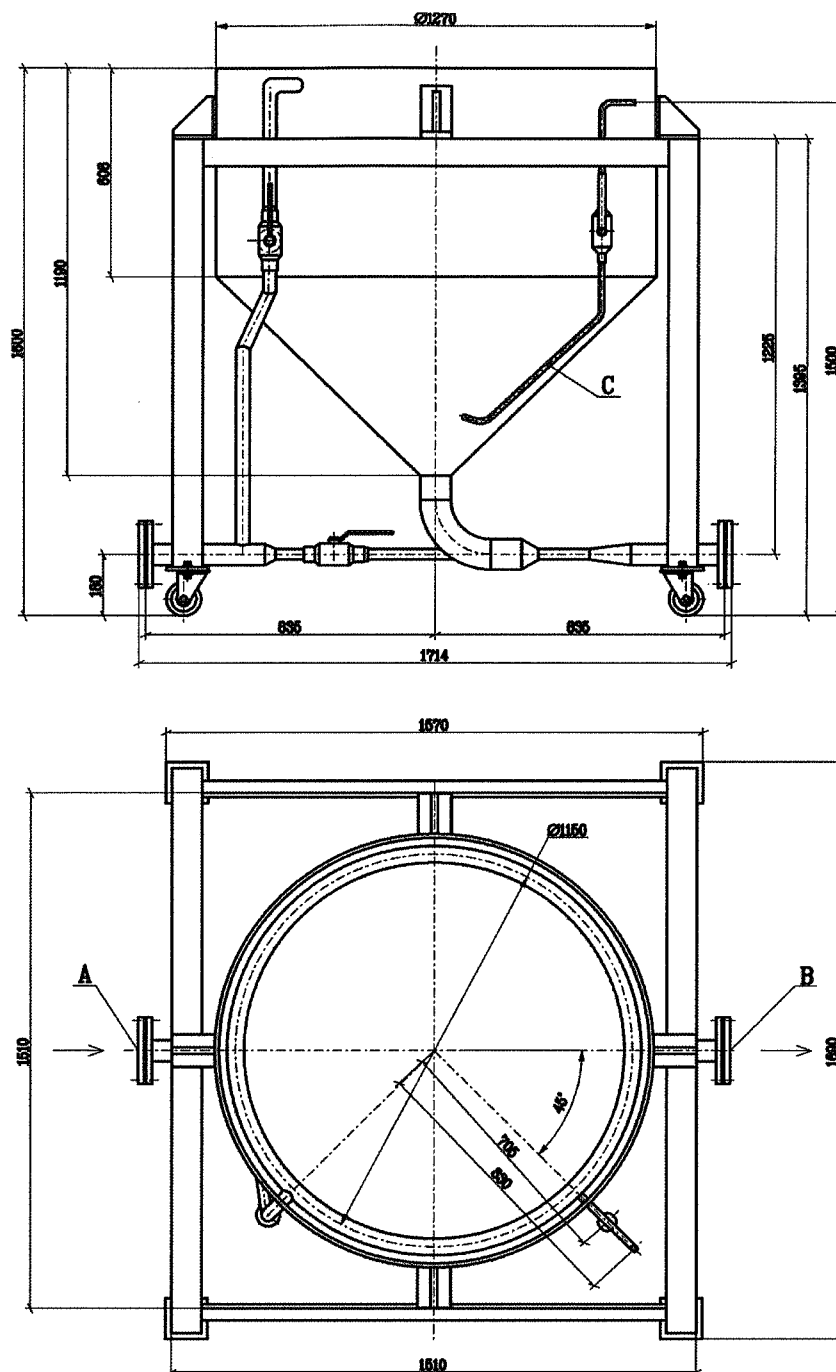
Габаритный чертеж гидротранспортера LDP01AF001
